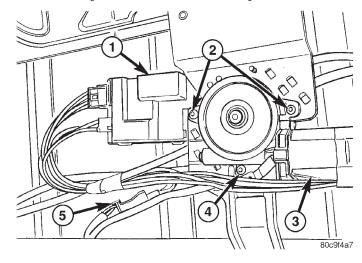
CONJUNTO DE MOTOR DE MANDO
